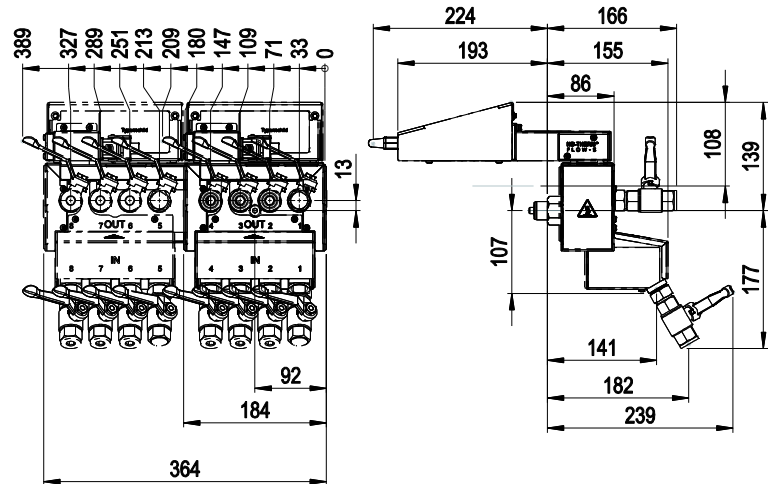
Dimensioner konstruktionsform: instrumentmontering Thermo-5
